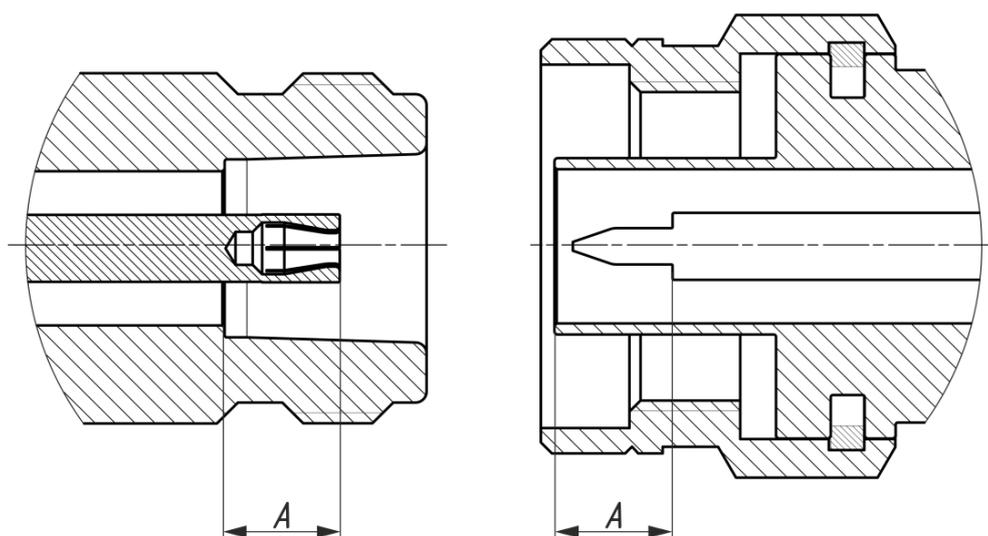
Соединители тип N и III (розетка и вилка)
